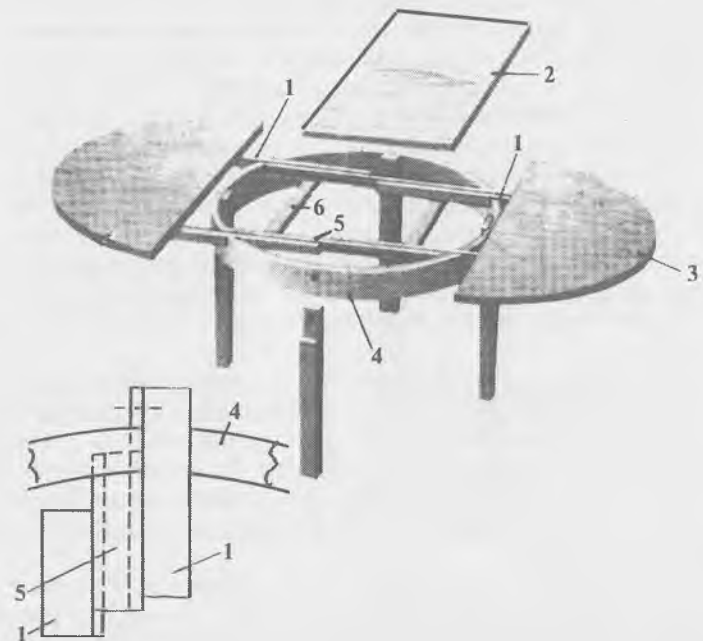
Конструкция стола с раздвижными крышками и нераздвижным круглым подстольем (круглой царгой):
